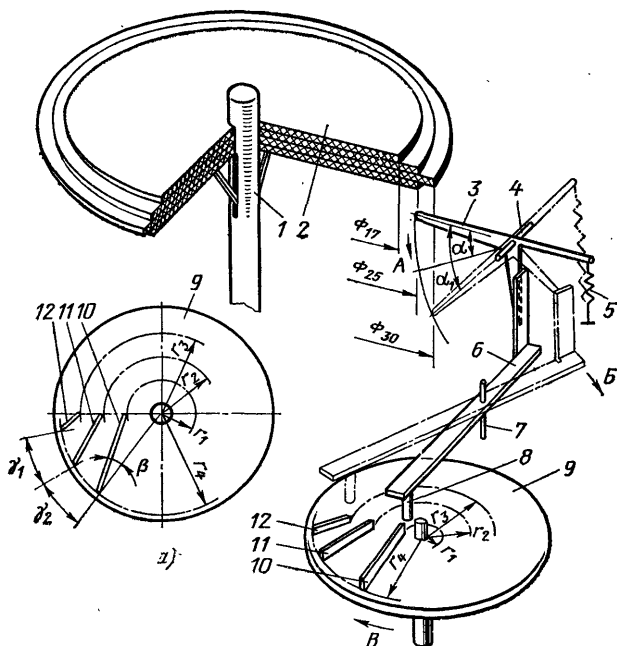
Кинематическая схема механизма автоматического переключателя габарита.
